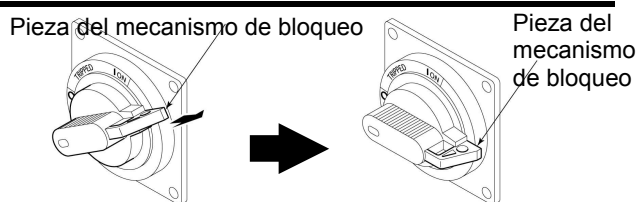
Extracción de la pieza del mecanismo de bloqueo
